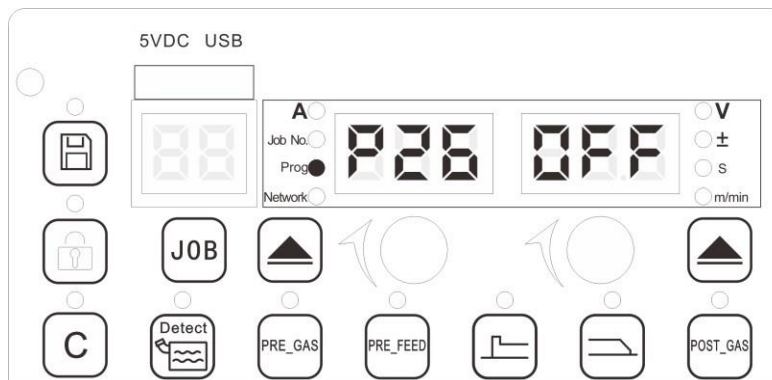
Активация режима сварки двумя проволоками "Tandem MIG" (P26)
